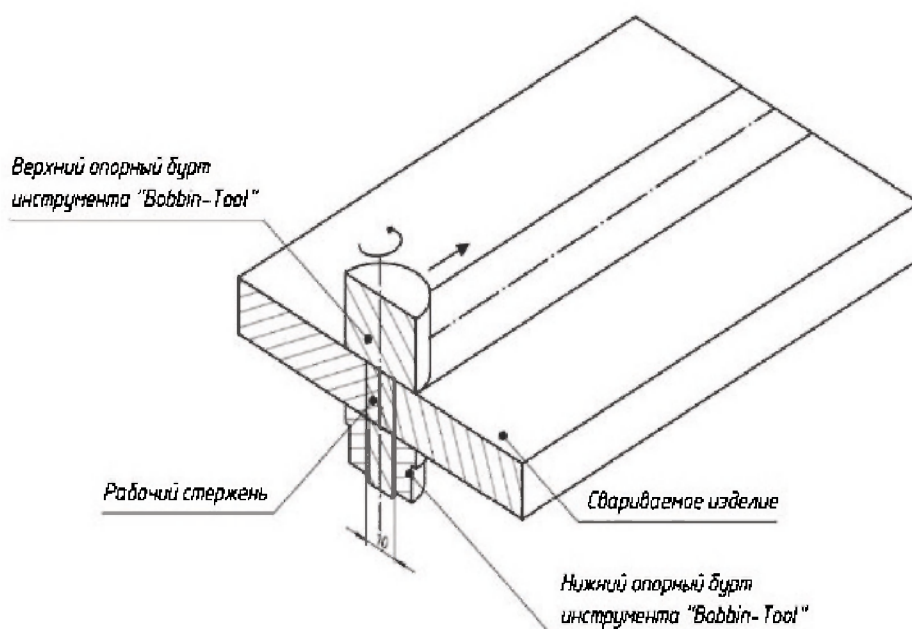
Схема процесса фрикционной сварки инструментом «Bobbin-Tool»
